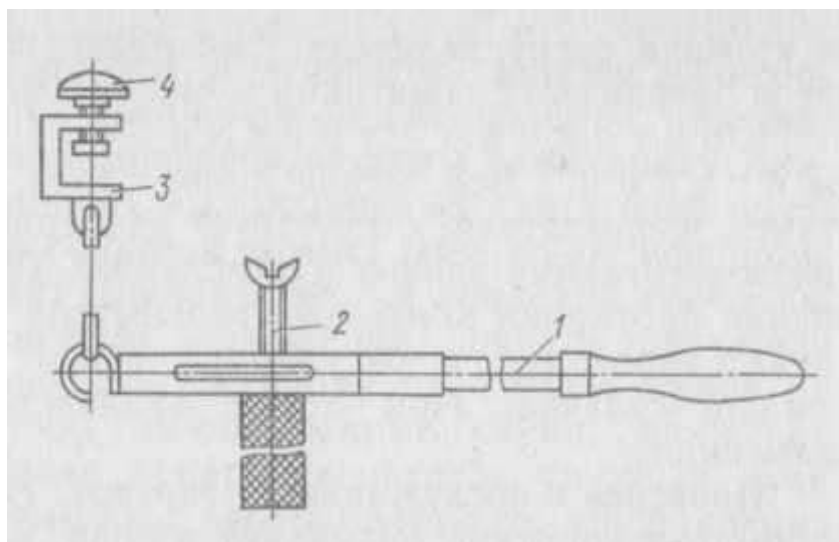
Приспособление для контроля усилия: 1 — универсальный рычаг; 2 — динамометр; 3 — струбцина; 4 — винт
